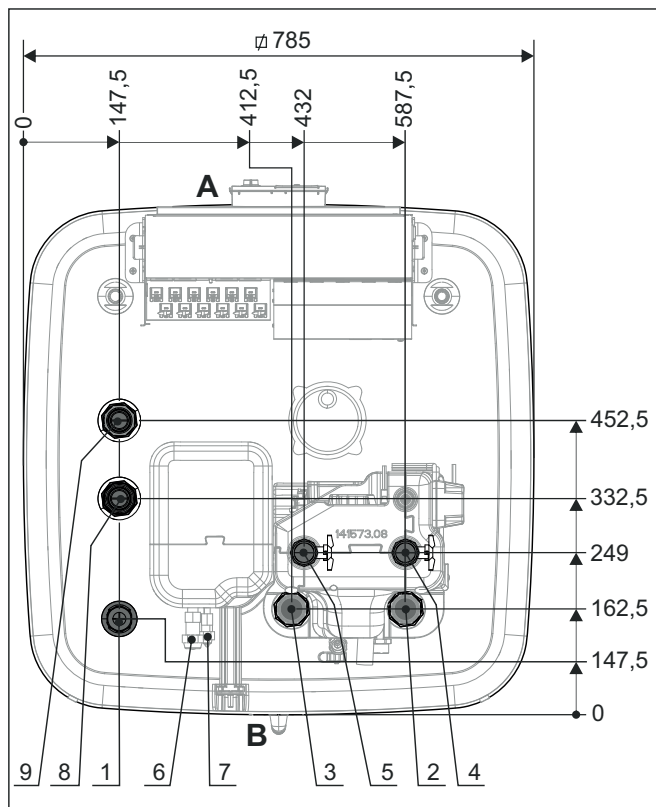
Dimensioni lato superiore dell'apparecchio - Tipo ... 04P50D/...08P50D
